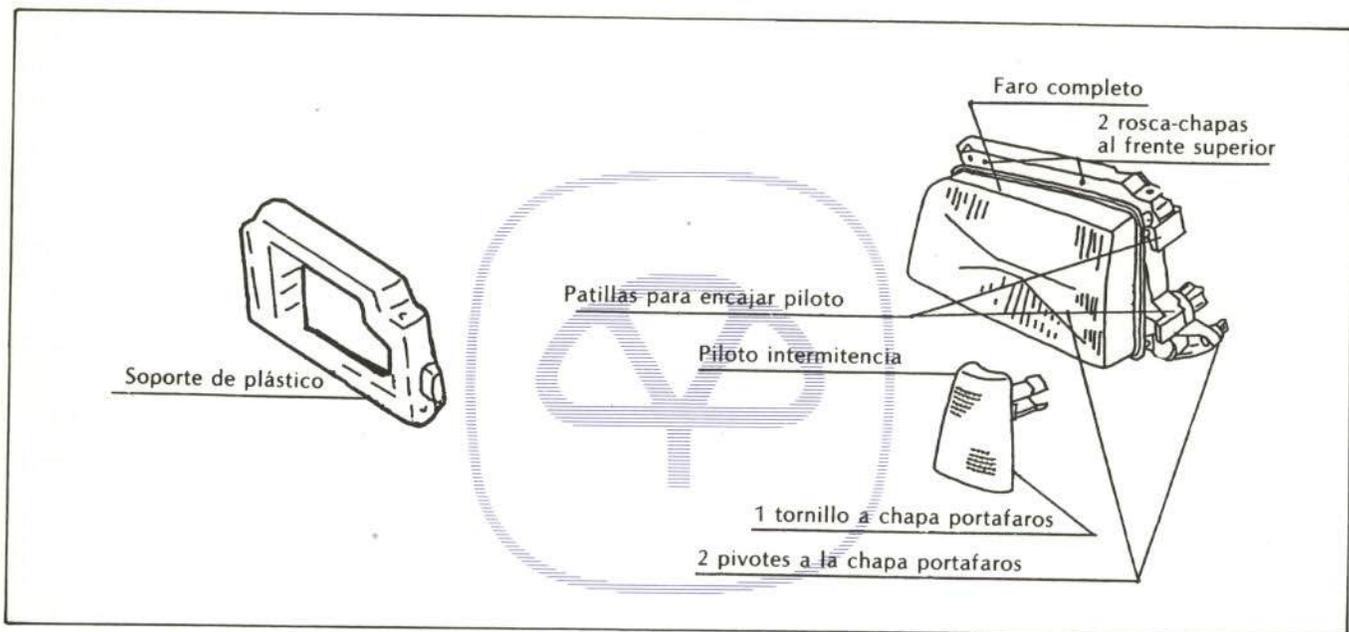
Fijación de faro y piloto a la carrocería. Repuesto del fabricante.
